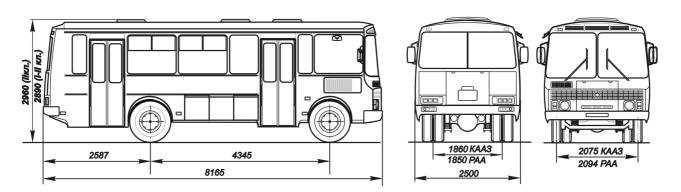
Габаритные размеры автобуса ПАЗ-4234
